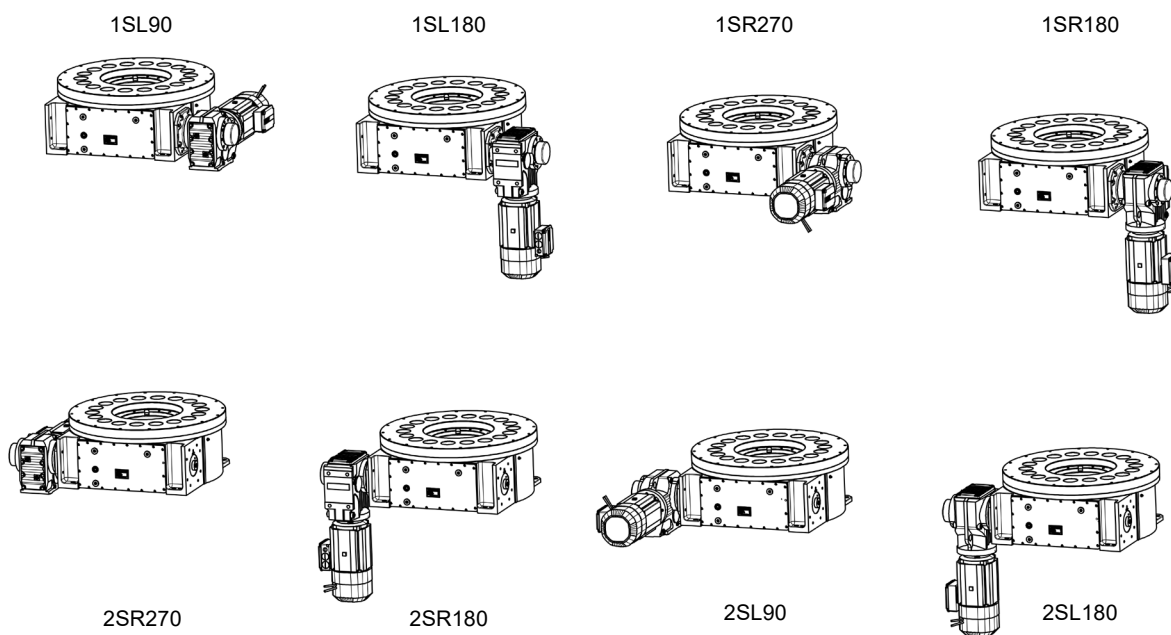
Posiciones de montaje del accionamiento TMF1000 - TMF5000
